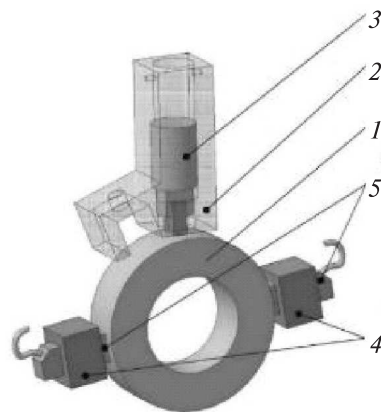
Модернизированный щеточно-контактный узел преобразователя ПО-250 А: 1 – контактное кольцо; 2 – дополнительный щёткодержатель под смазывающую щетку; 3 – смазывающая щётка; 4 – штатный щёткодержатель; 5 – испытываемые щетки
